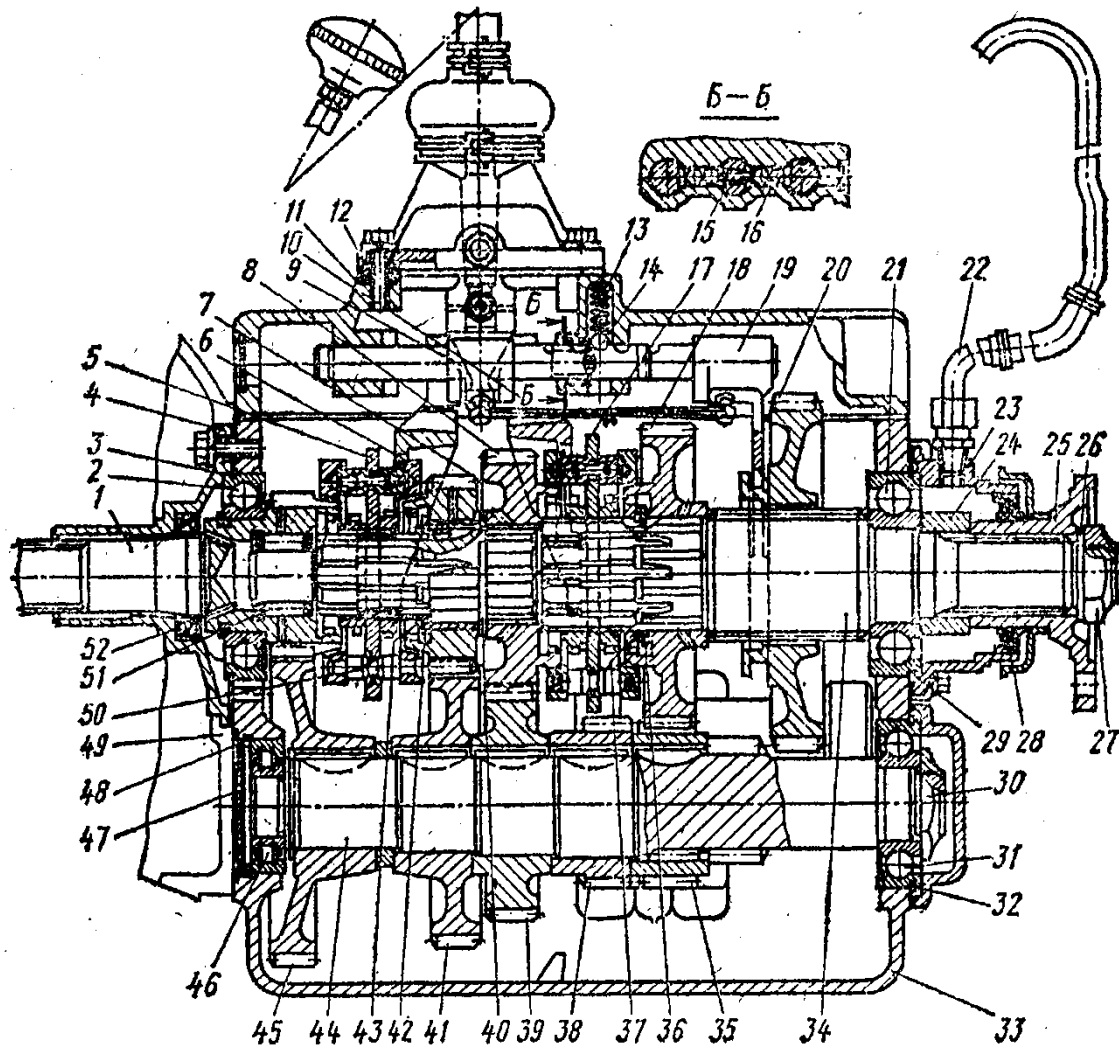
Коробка передач ЗІЛ-130 (поперечний розріз):
